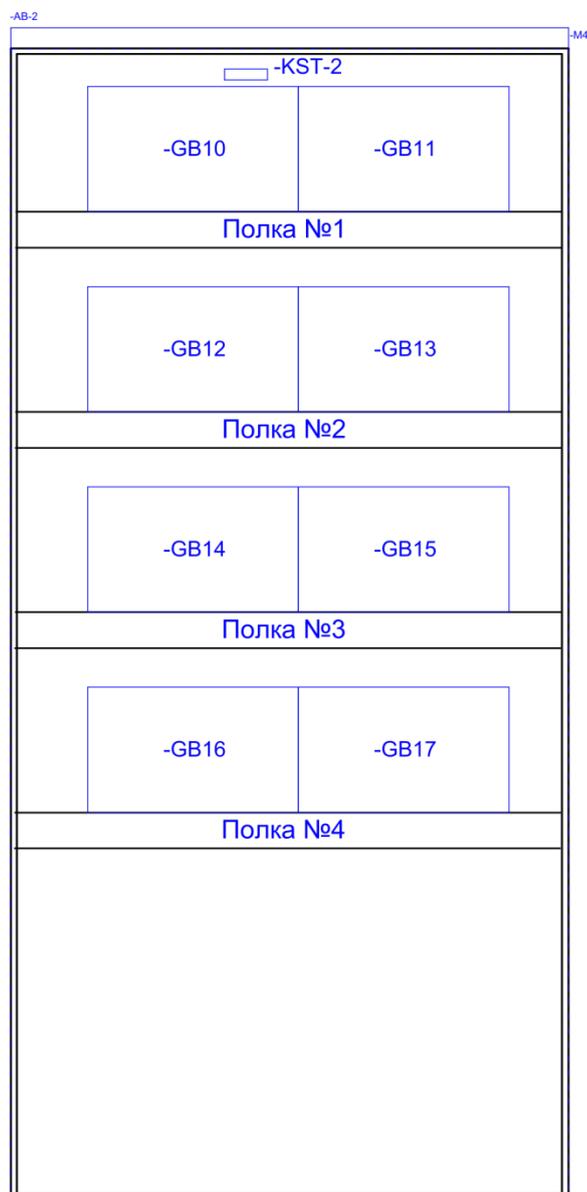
Сборочный чертеж с одним шкафом аккумуляторных батарей
